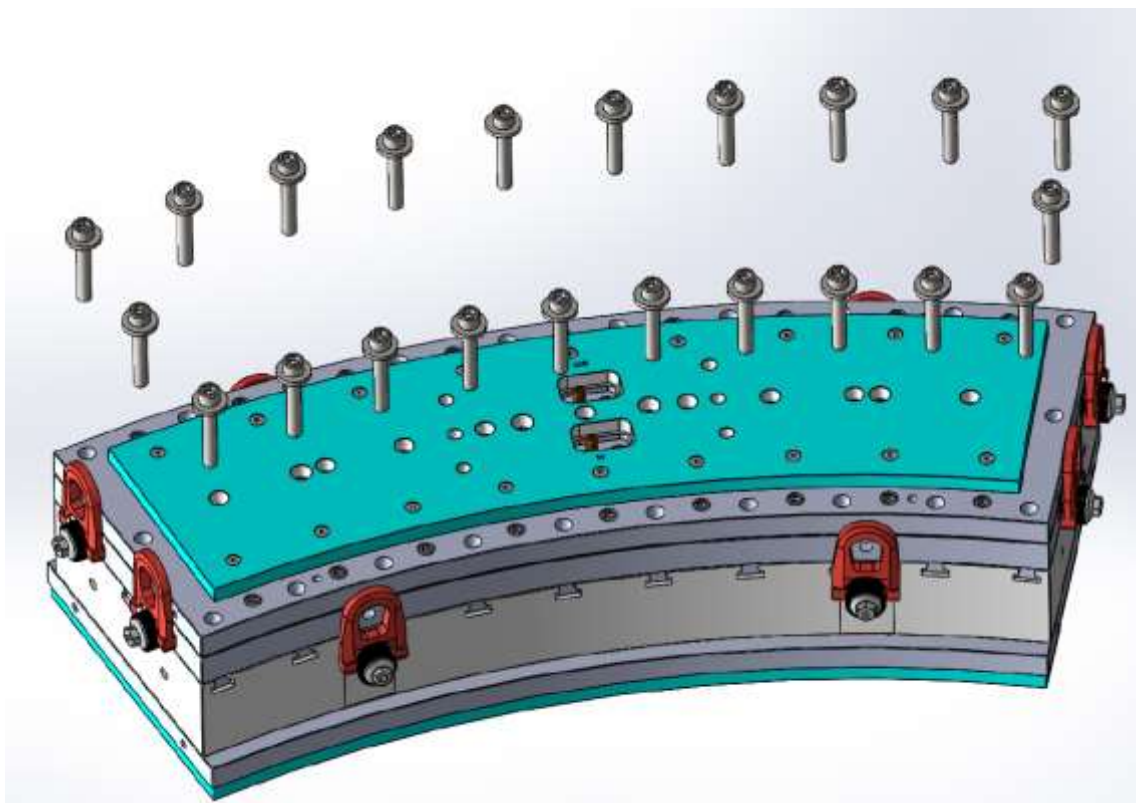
Sistema de cierre por tornillos en el molde RTM, el cual incluye 22 tornillos de M16 x 80 mm (DIN 912 12.9) y una distancia entre tornillos de 115 mm.
